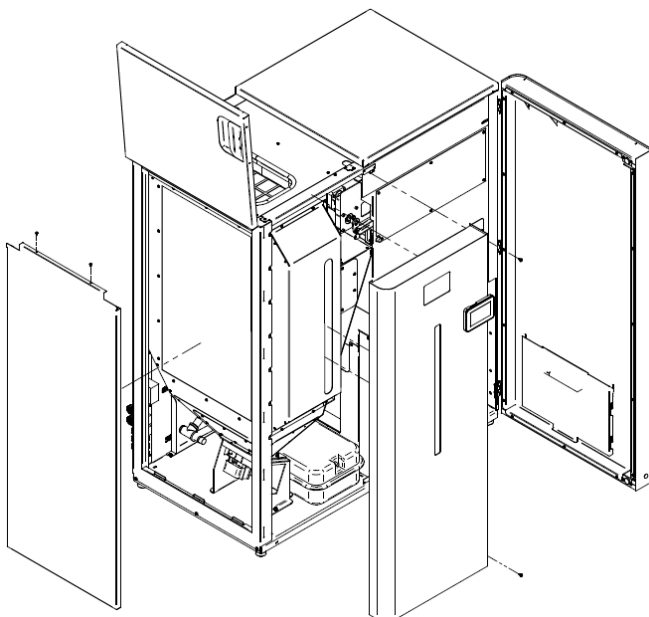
Extracción de los tornillos que fijan la parte frontal de la caldera
